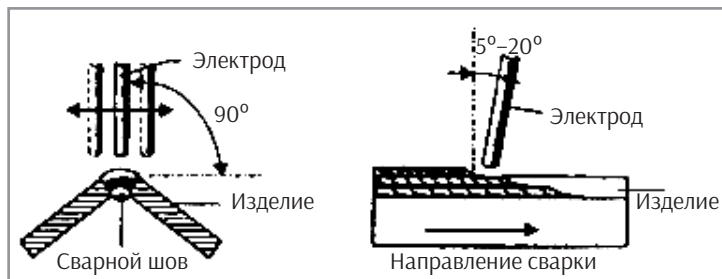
Положение электрода при сварке углового соединения с наружным углом в нижнем положении
